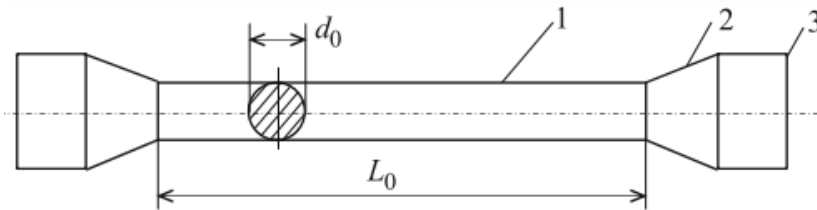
Циліндричний зразок (1 – робоча частина; 2 – перехідна частина; 3 – захвати; L_0 – розрахункова довжина (база); d_0 – діаметр бази)
